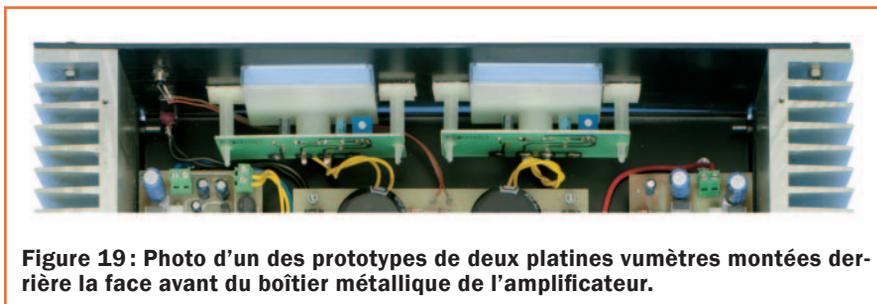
Photo d'un des prototypes de deux platines vumètres montées derrière la face avant du boîtier métallique de l'amplificateur.
